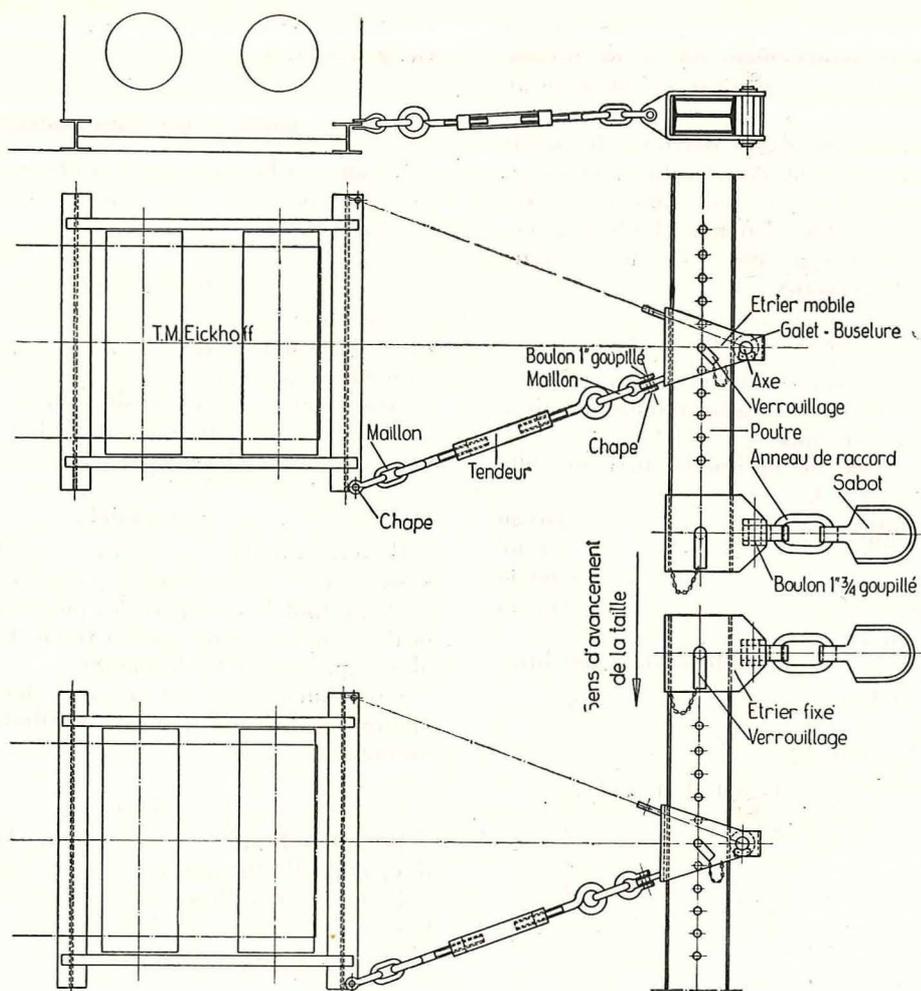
et 26. — Dispositif de fixation des têtes motrices.
